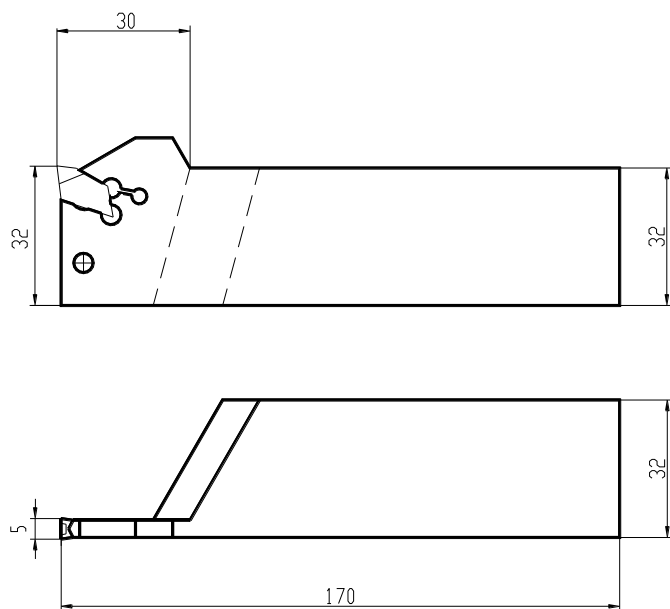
Отрезной резец со сменной твердосплавной пластиной
